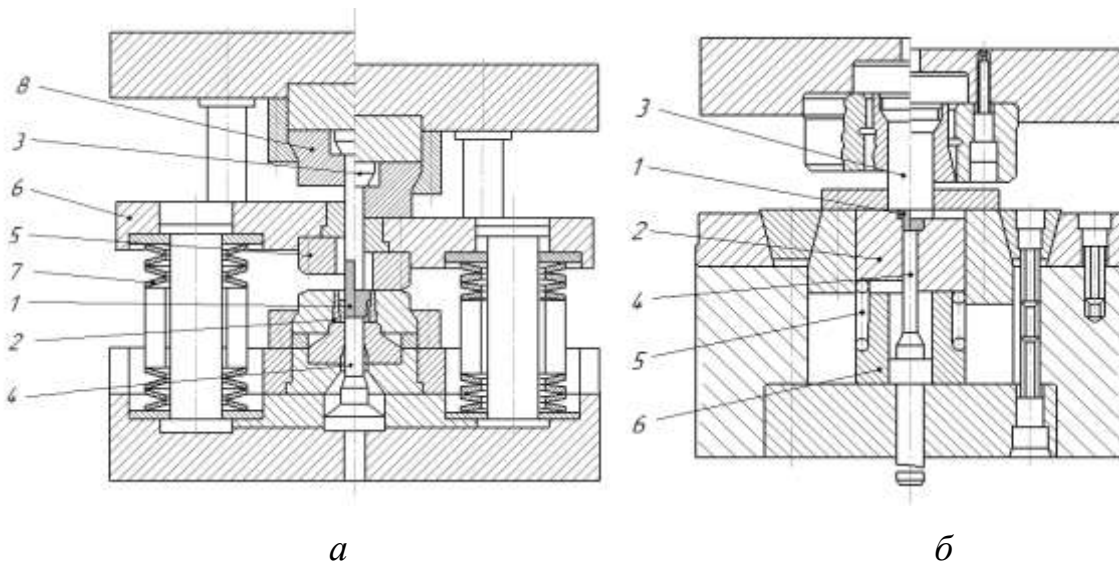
Варіанти конструкцій штампів для калібрування різних заготовок способом радіального видавлювання
